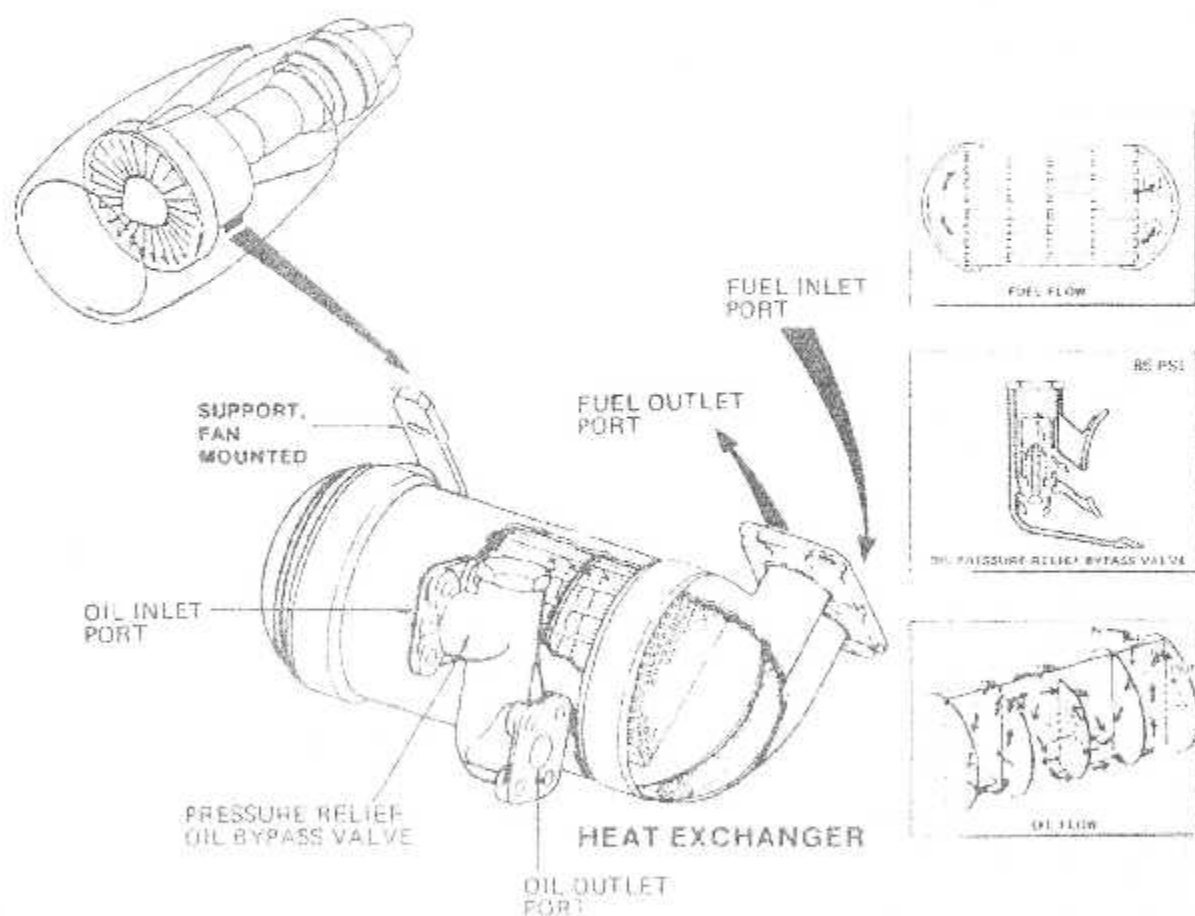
ECHANGEUR THERMIQUE PRINCIPAL CARBURANT/HUILE REACTEUR
